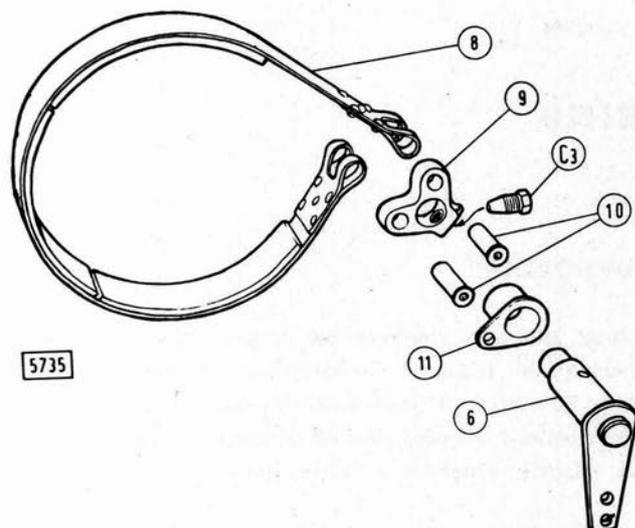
Parties démontées d'un ensemble de freinage.
